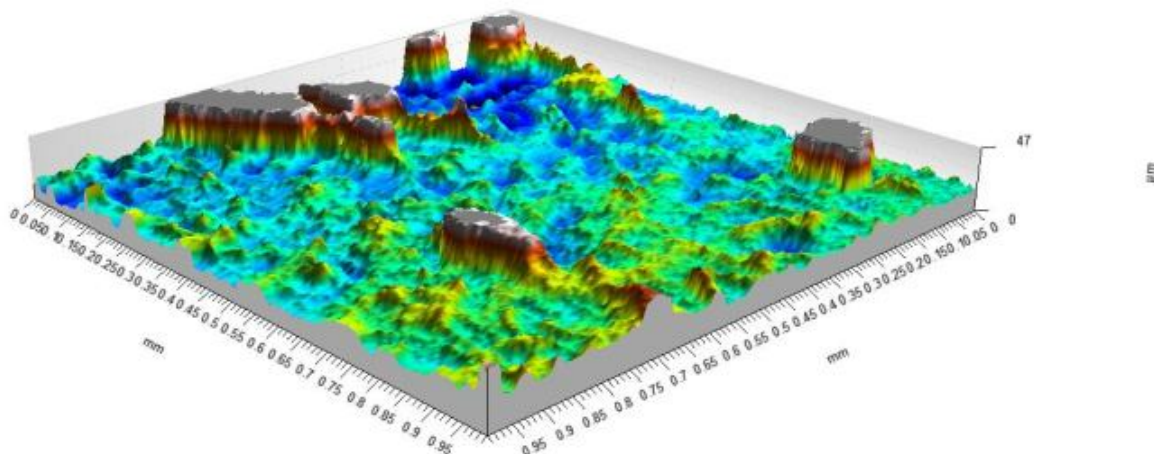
2D zobrazení broušeného povrchu oceli 11 600
